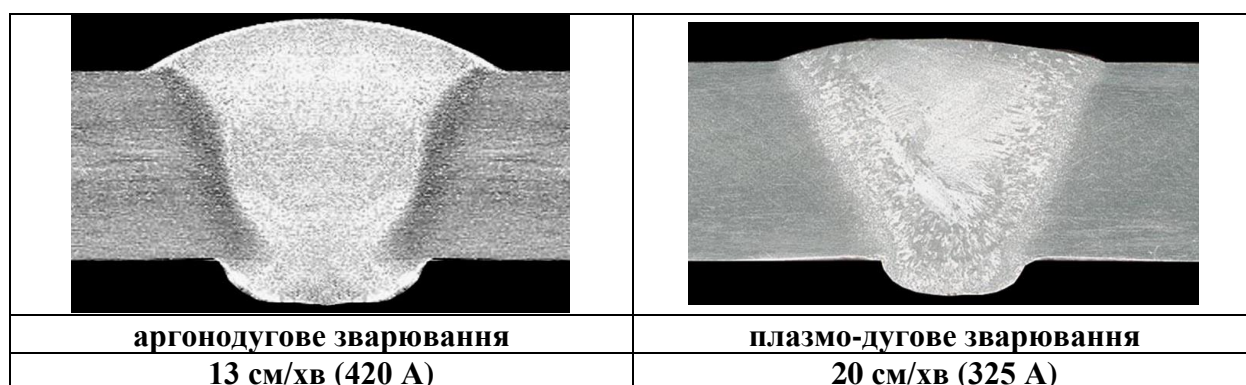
Поперечні шліфи зварного з'єднання листів товщиною 10,0 мм із сплаву АМг6Н отриманих різними способами зварювання неплавким електродом з використанням присадкового дроту СвАМг6.
